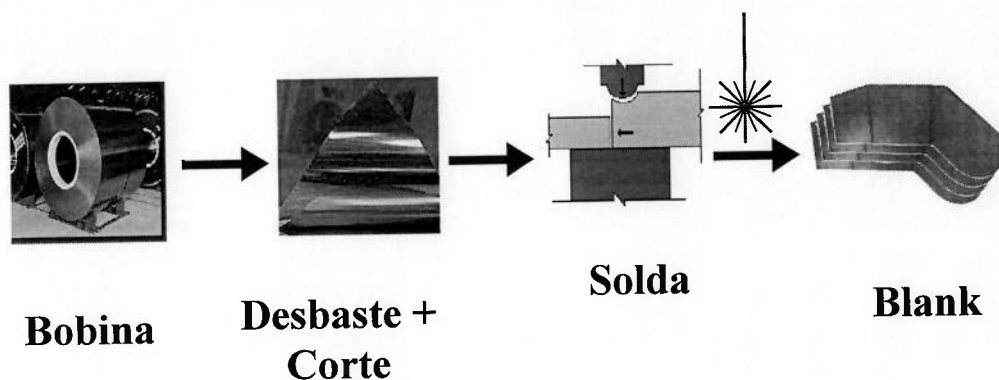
Processo de fabricação de Blank Soldado.
